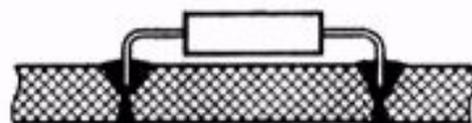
Установка и пайка ЭРИ с плоскими планарными выводами, формованными для установки в глухое круглое монтажное отверстие и пайки встык
